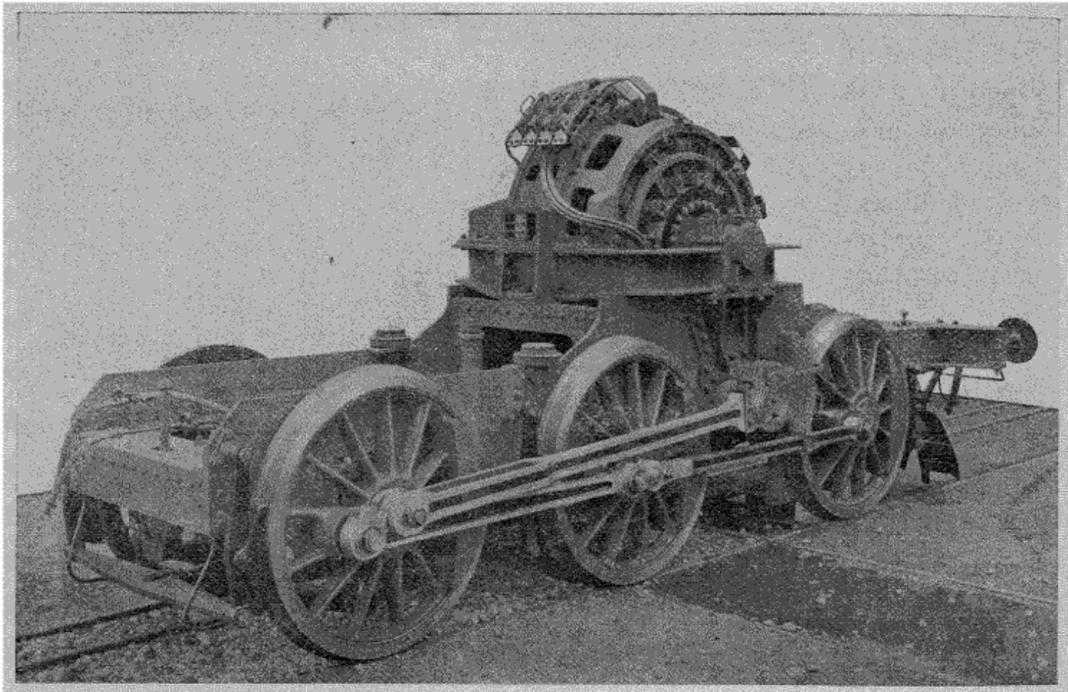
Vue d'un bogie de la locomotive d'Oerlikon.
